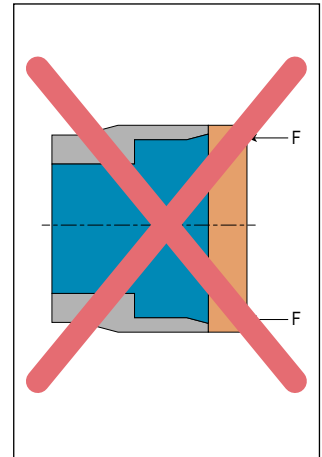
Application incorrecte de la force d'emboîtement sur la tulipe femelle
